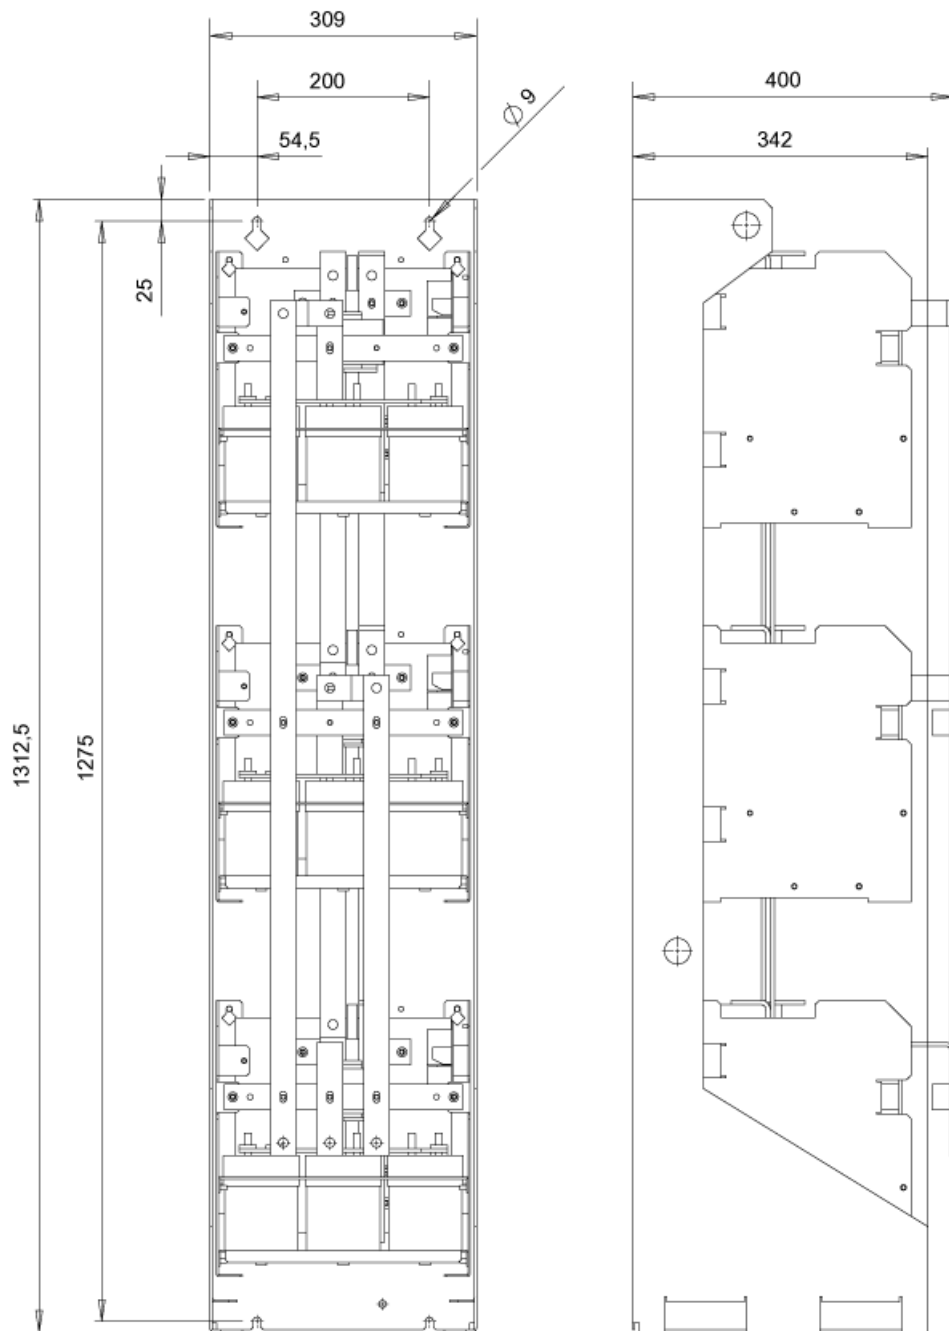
Габаритный чертеж схемы ограничения напряжения, тип 3
